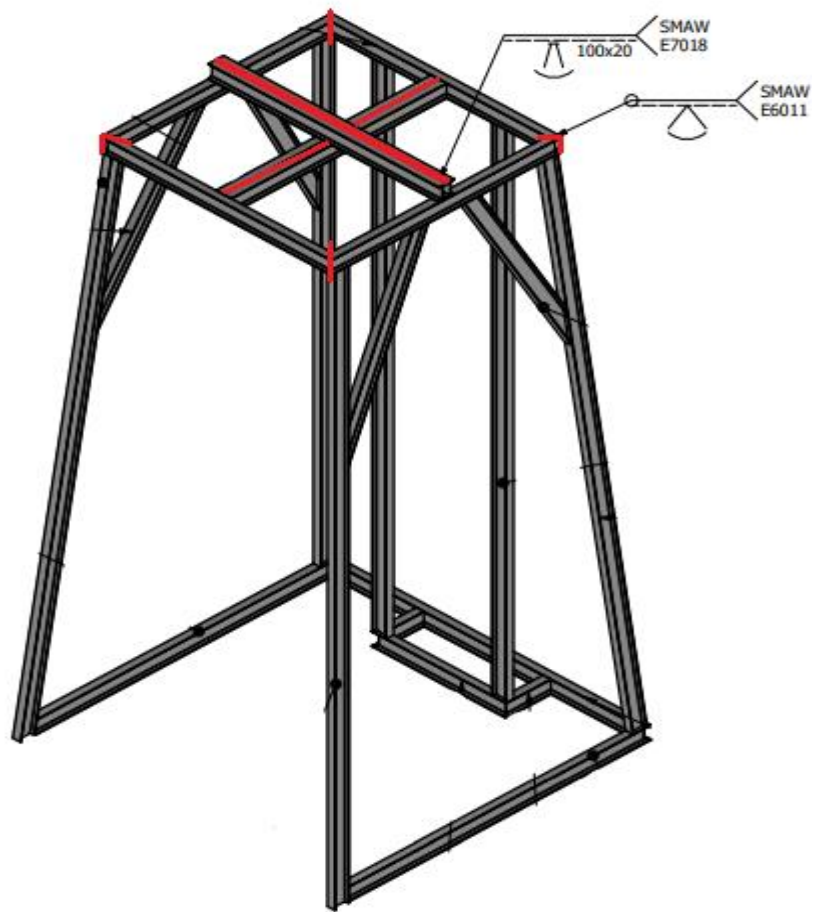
6. Diseño de soldadura del sistema estructural
